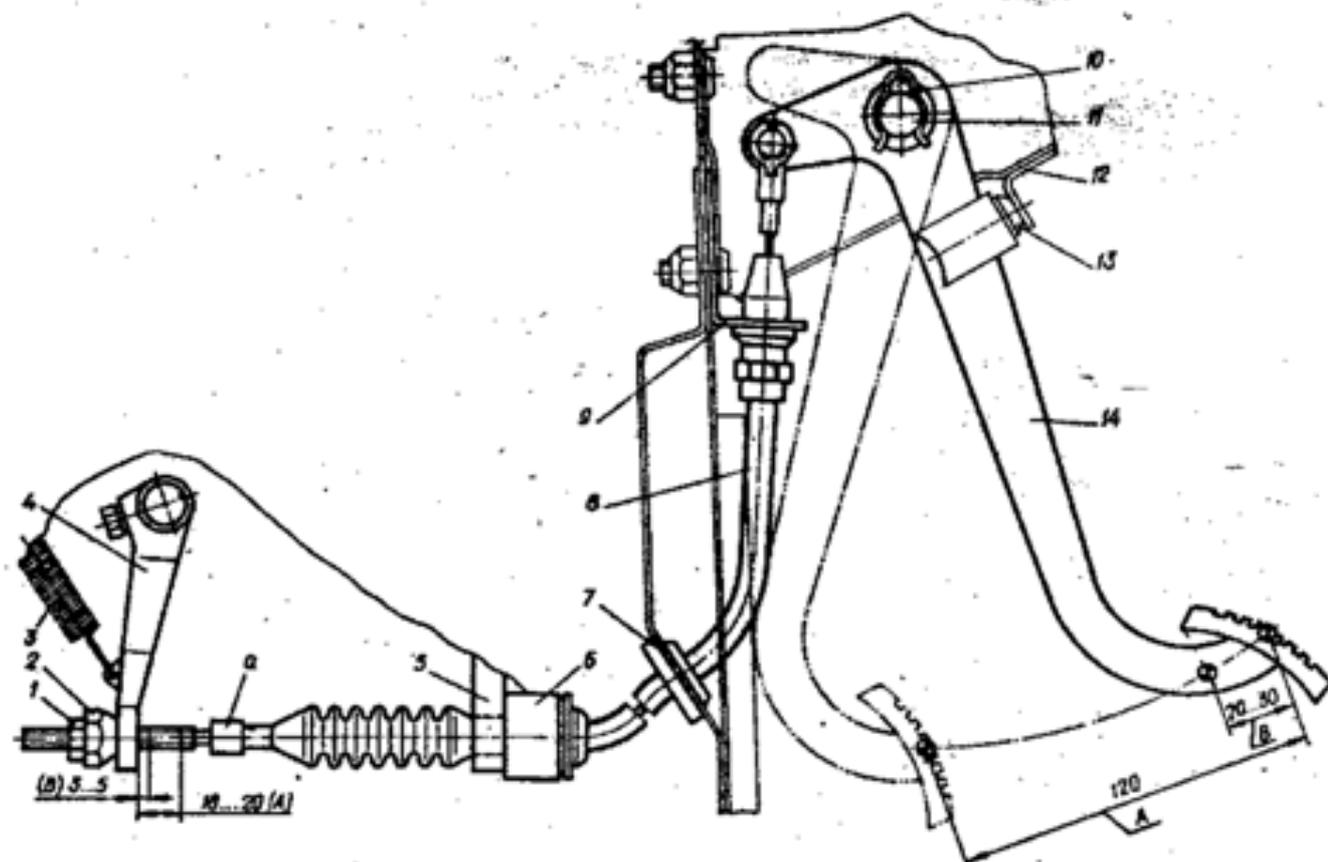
Привод выключения сцепления: 1 - контргайка; 2 - гайка регулировочная; 3 - пружина; 4 - рычаг оси; 5 - упор на картере; 6 - демпфер; 7 - уплотнитель; 8 - трос в сборе; 9 - упор на кузове; 10 - защелка; 11 - ось педалей; 12 - упор педали; 13 - буфер; 14 - педаль сцепления; В - свободный ход педали; А - полный ход педали
